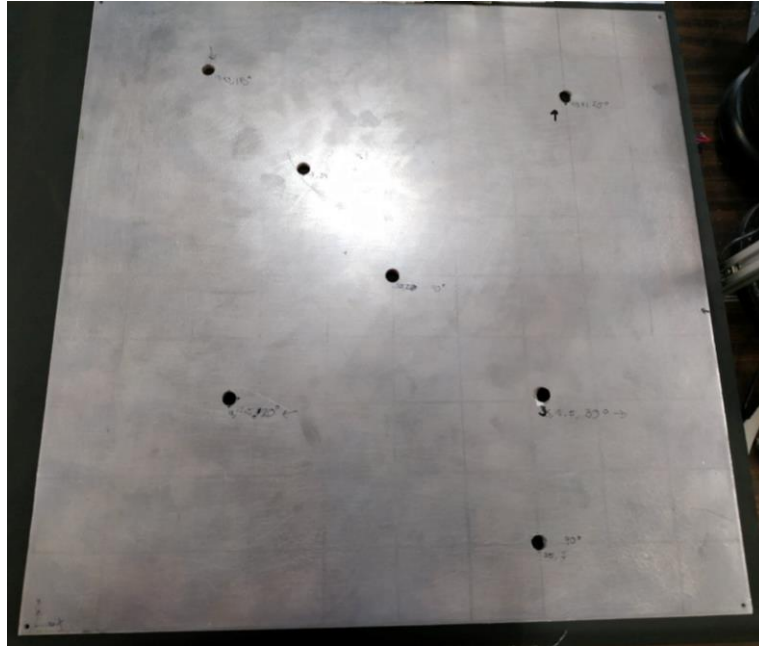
FOTO DE PLACA CON LOS BARRENOS DE PRUEBA
